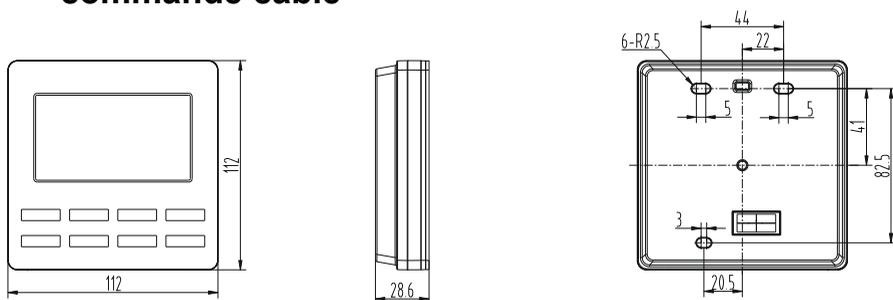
Dimensions du panneau de commande câblé (en mm)
